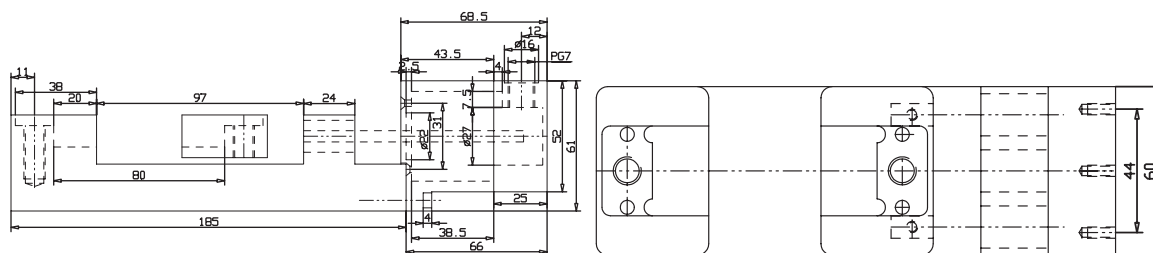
Technische Zeichnung der Einspannvorrichtung für die mechanische Stimulation. Links: Seitenansicht mit Motorblock. Rechts: Aufsicht ohne Motorblock.
